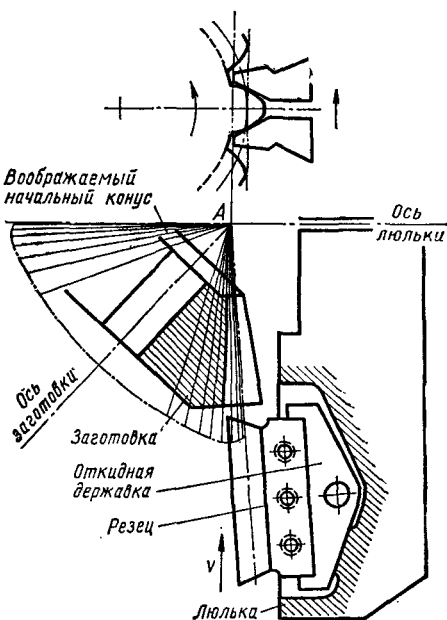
Схема обработки прямозубых конических колес на зубострогальном станке
